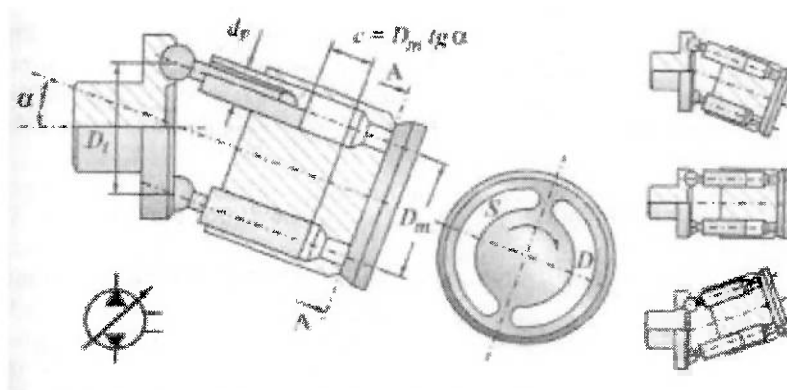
Esquema de máquina de pistões axiais de eixo inclinado
